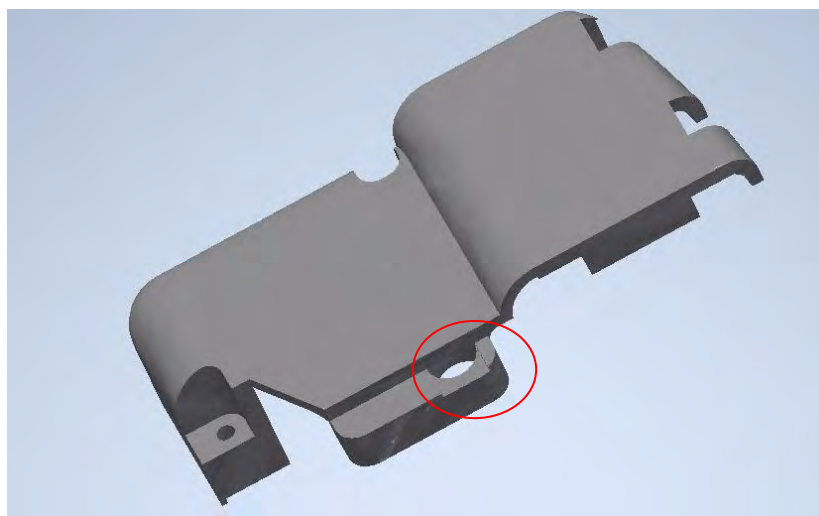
Tapa izquierda de la palma, En el círculo rojo se observa las modificaciones de la tapa de la palma para el ensamble del sensor de efecto Hall
